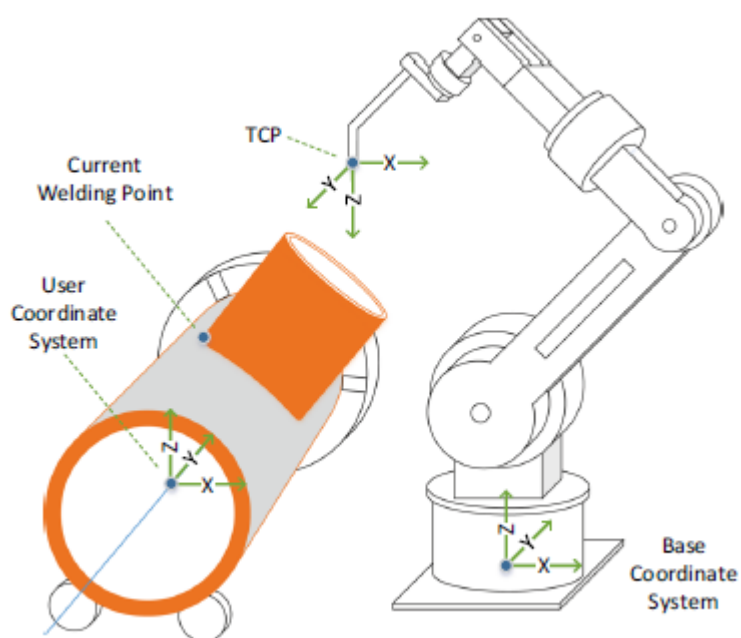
Ilustração da soldadura da interseção de tubos por um manipulador industrial [30].
